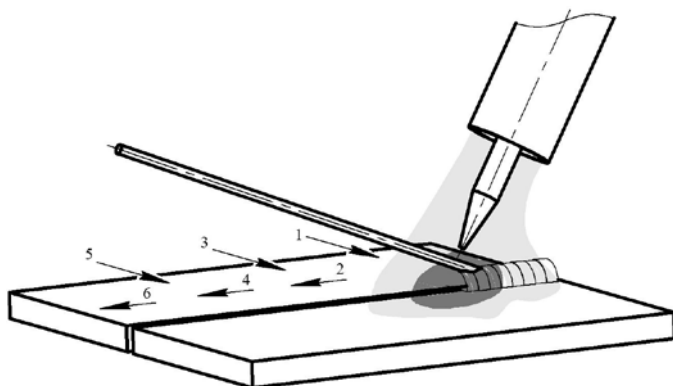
Пример манипуляции присадочной проволокой при TIG сварке.
